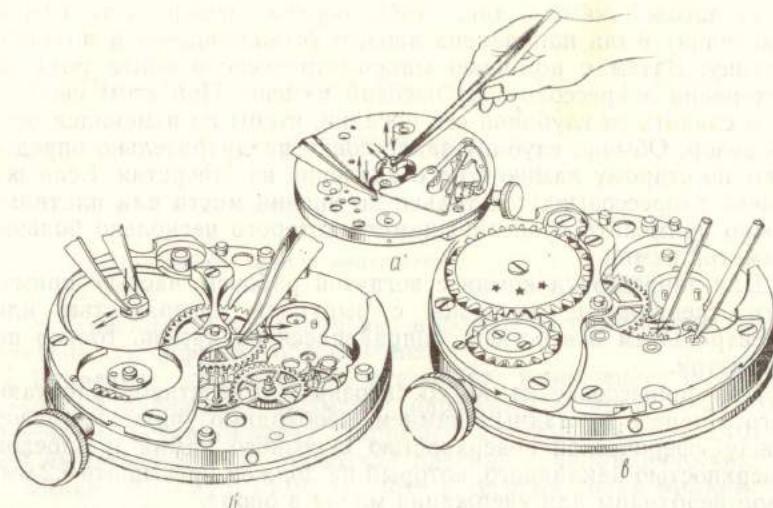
Способы проверки зазоров в часовом механизме: а — центрального и секундного колес; б — барабана и центрального колеса; в — зацепленных колес ангренажа в собранном механизме.
